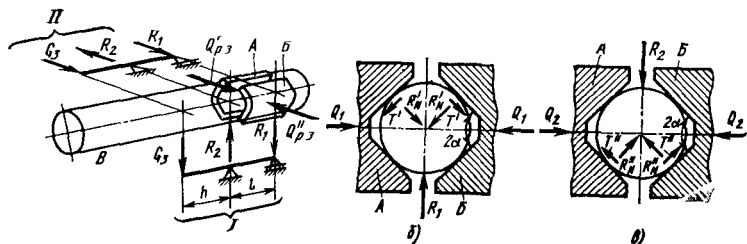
Схема расчета захвата для длинномерных заготовок
